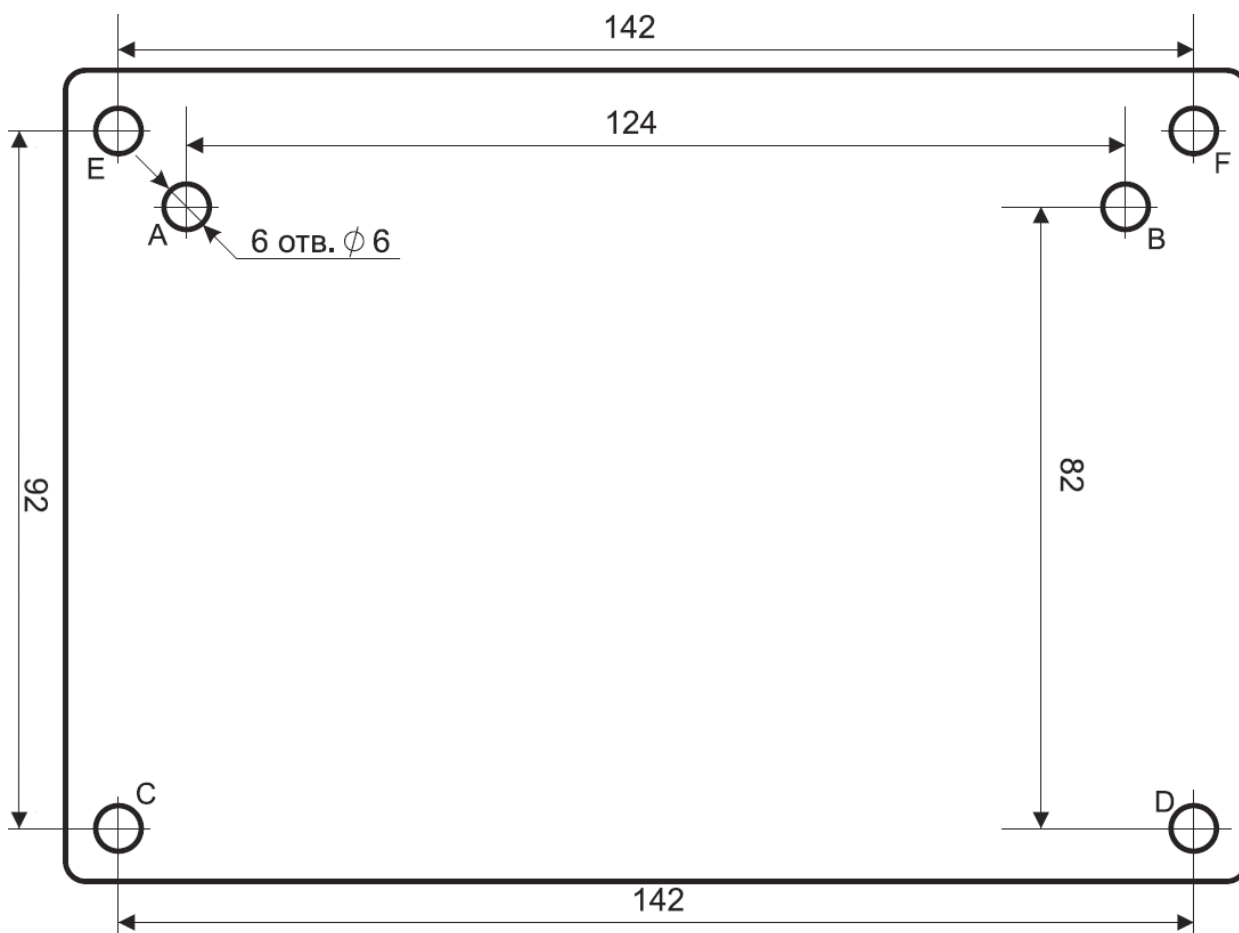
Схема сверловки для монтажа блока на стену.
